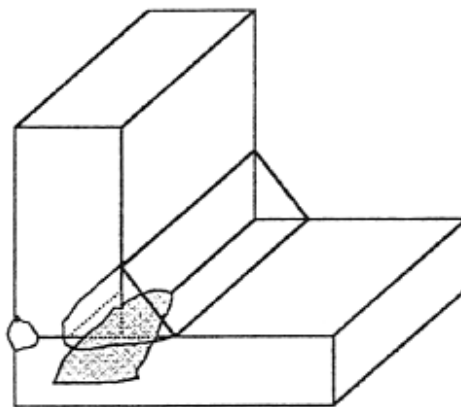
GRIETAS BAJO EL CORDÓN
